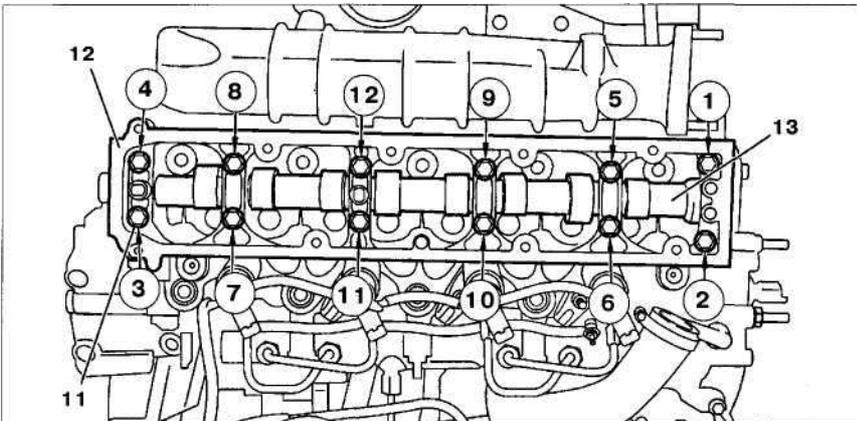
Порядок откручивания болтов 11 крепления корпуса распределительного вала. Снимите корпус 12 распределительного вала, распределительный вал 13 и прокладку.
